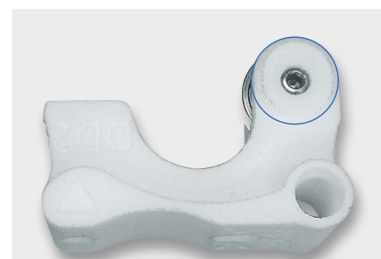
Gewindebolzen statt Bolzen – der mitgelieferte Gewindebolzen ist eindeutig die elegantere Lösung.
